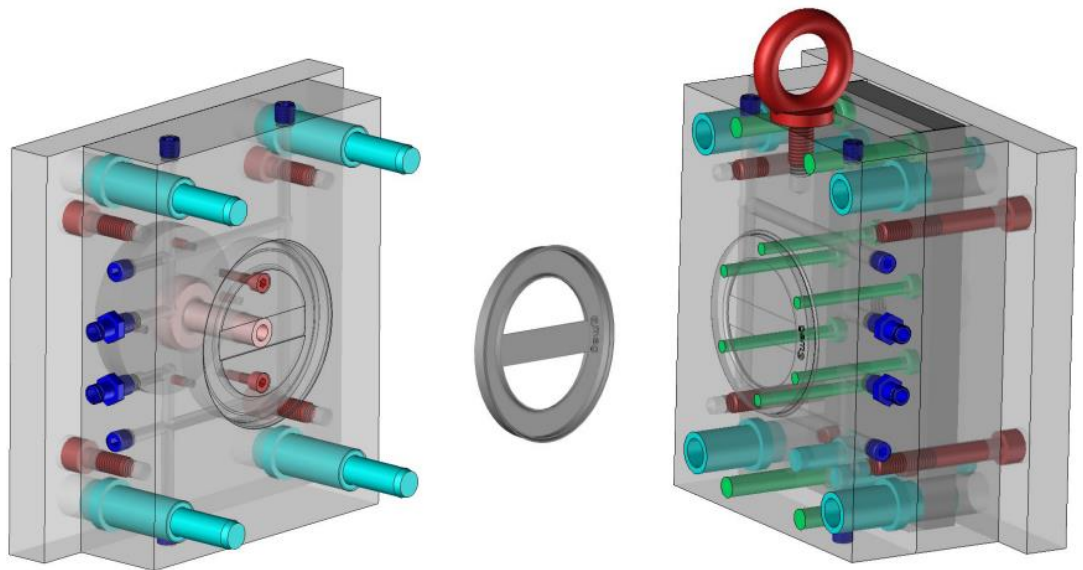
MOLDES DE INYECCIÓN DE 2 PIEZAS
